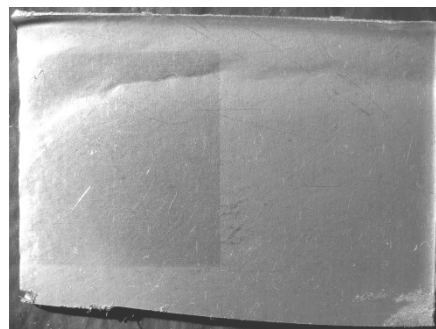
Внешний вид трёхслойного образца TiNi-сталь со стороны стали
